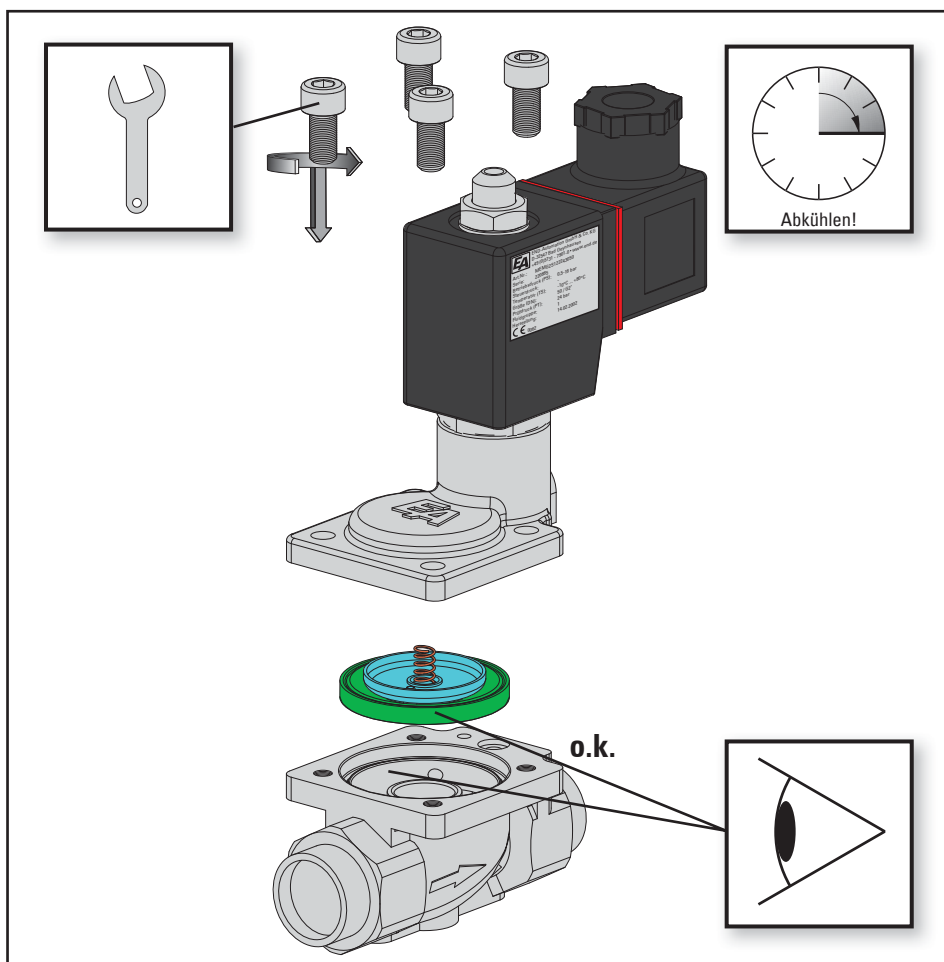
Einbau: Anschweißenden, montieren des Ventiloberteils
